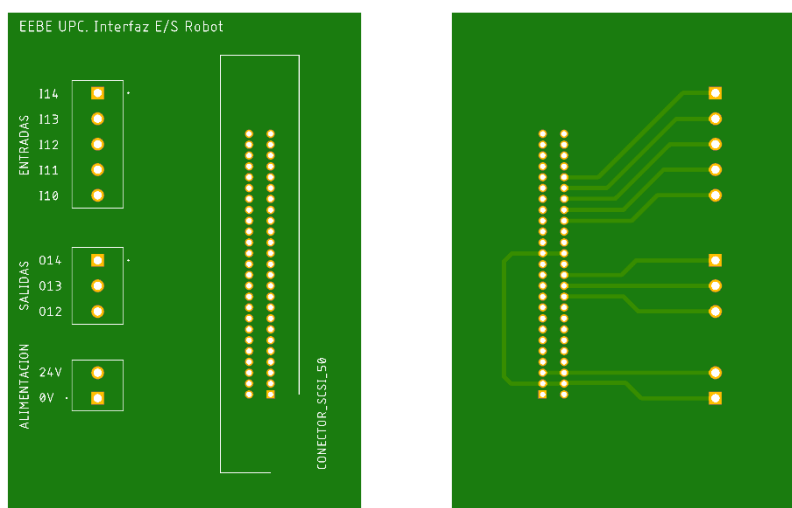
Diseño final de la placa PCB (escala 1:1,5)
